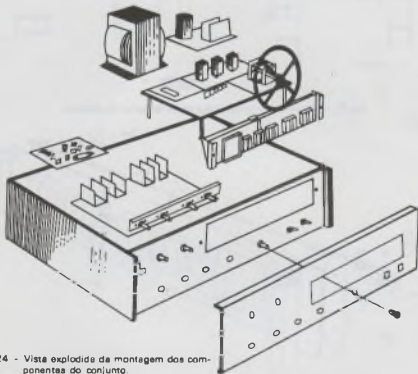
Vista explodida da montagem dos componentes do conjunto.
